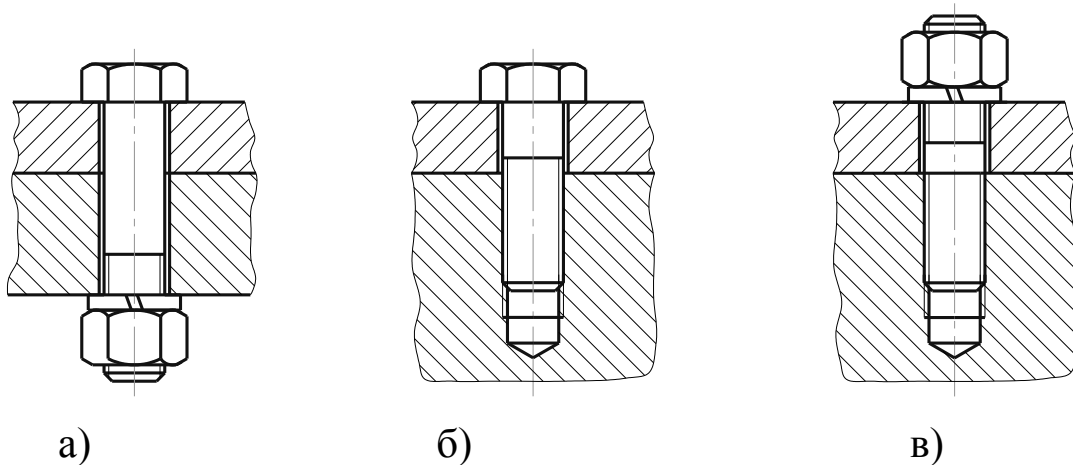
Резьбовые соединения: а – болтом; б – винтом; в – шпилькой
